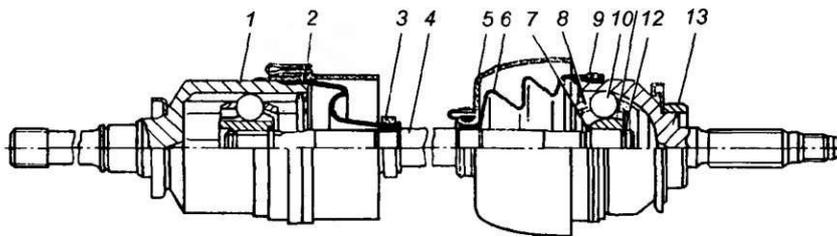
Привод передних колес: 1 — корпус внутреннего шарнира; 2 — фиксатор внутреннего шарнира; 3 — кольцо крепления чехла; 4 — ; 5 — защитный кожух чехла; 6- защитный чехол; 7 упорное кольцо обоймы; 8 — сепаратор; 9 — хомут; 10 — шарик; 11 — обойма; 12 — стопорное кольцо обоймы; 13 — корпус наружного шарнира
